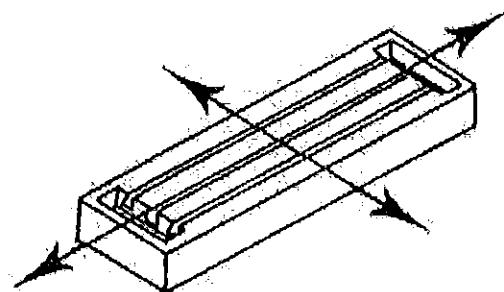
ลักษณะและส่วนต่างๆของ VERTICAL MILLING MACHINE
